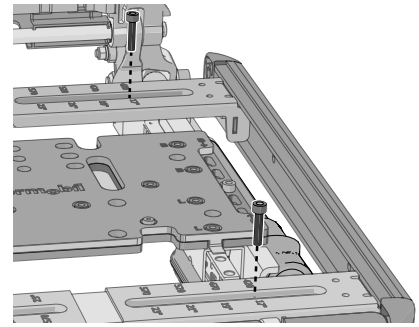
Die UniTrack-Schienenhalterungen werden mit zwei Schrauben befestigt.
